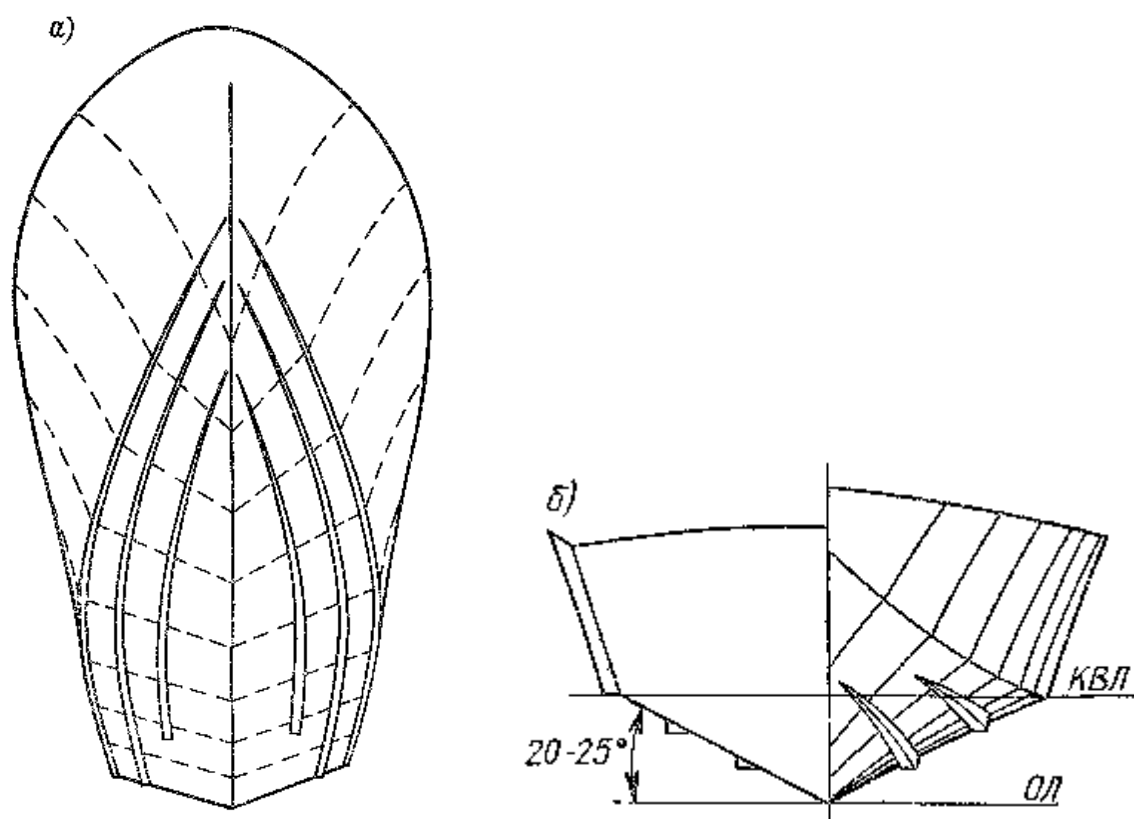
Обводи типу «Глибоке V». а – вид на днище; б - корпус теоретичного чертежа.
